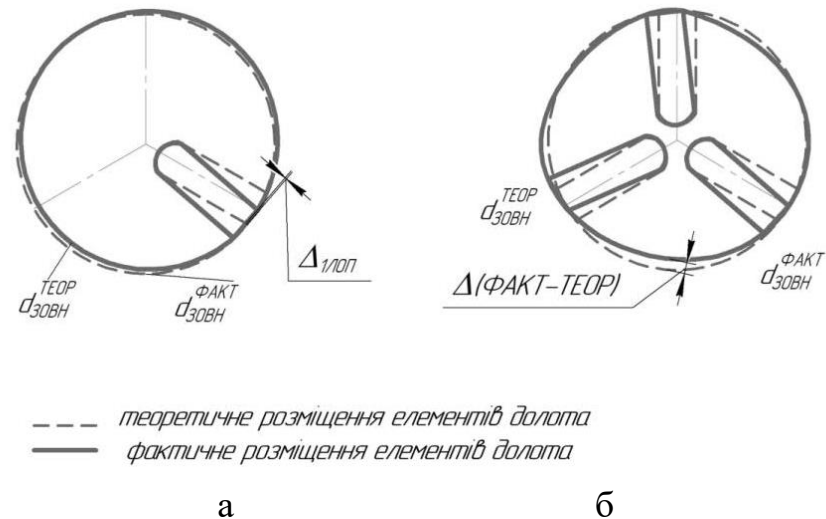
Формування похибок зовнішнього діаметра долота під час приварювання лопатей до корпусу долота однієї лопаті (а) та трьох лопатей (б)
